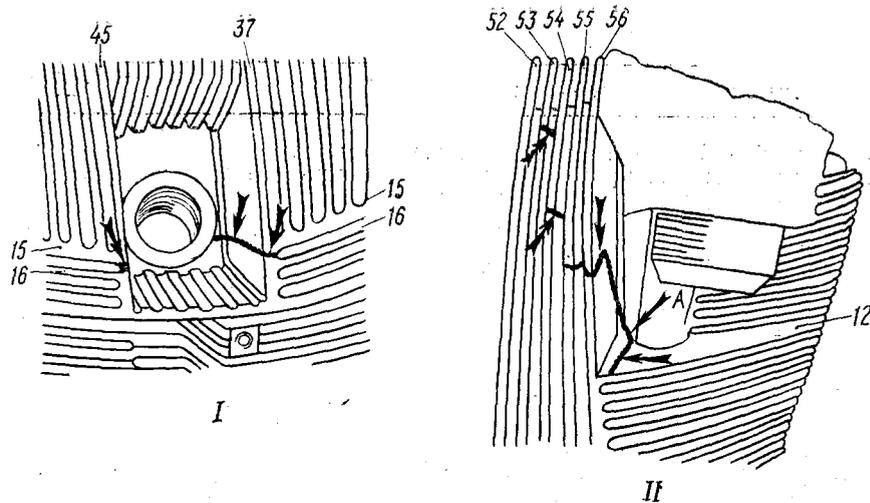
Характерные места образования трещин на головках цилиндров: I — на боковой и торцевой поверхностях вертикальных ребер 37 и 45 и гнезда футорки задней свечи. Цифрами обозначены номера соответствующих ребер охлаждения головки цилиндра; II — на клапанной коробке выпуска. Стрелкой А указано место возникновения трещины. Остальными стрелками — трещины на горизонтальном ребре 12 и вертикальных ребрах 52 ... 56
